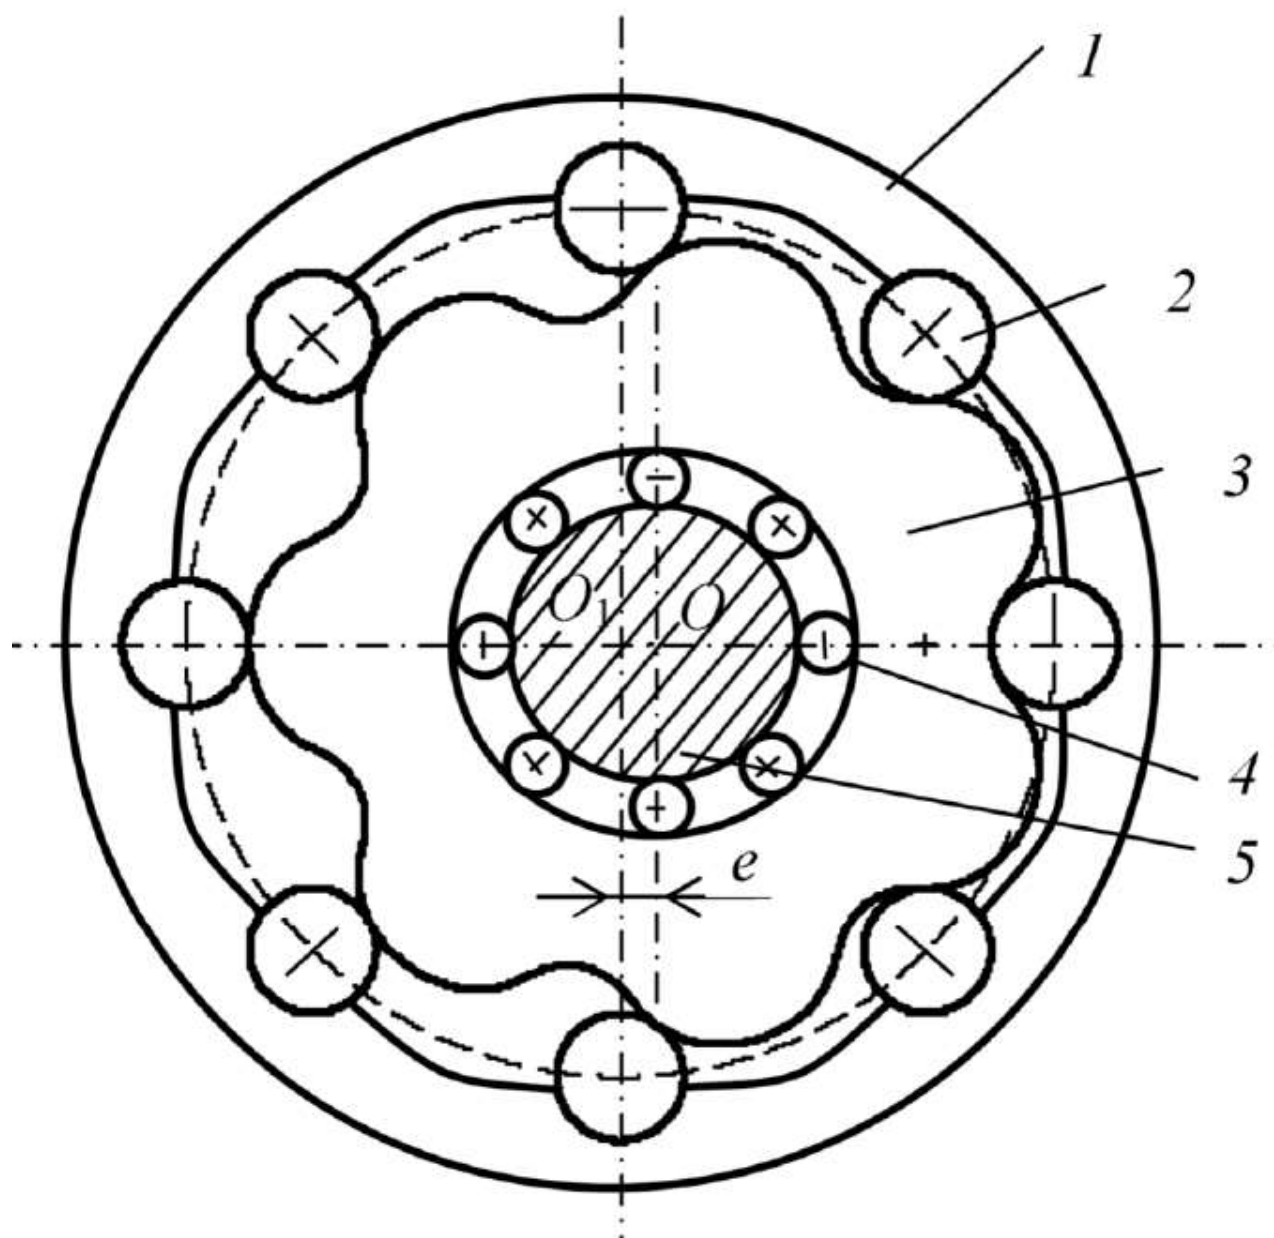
Схема планетарно-цівкової передачі [14, 16 32, 35, 37, 42, 43]: 1 - цівкове колесо; 2 - цівки; 3 - сателіт; 4 - роликовий підшипник; 5 - ексцентрик
